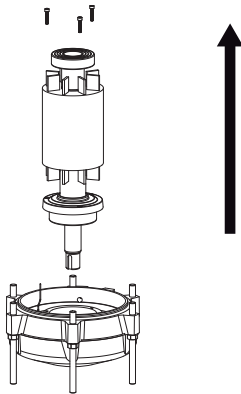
Dépose de l'ensemble rotor (J 205, J 405)
